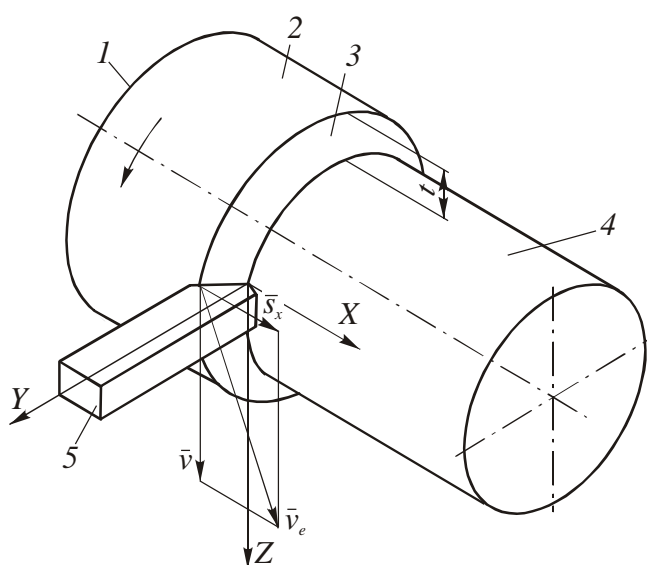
Кинематическая схема процесса продольного точения токарным проходным резцом
